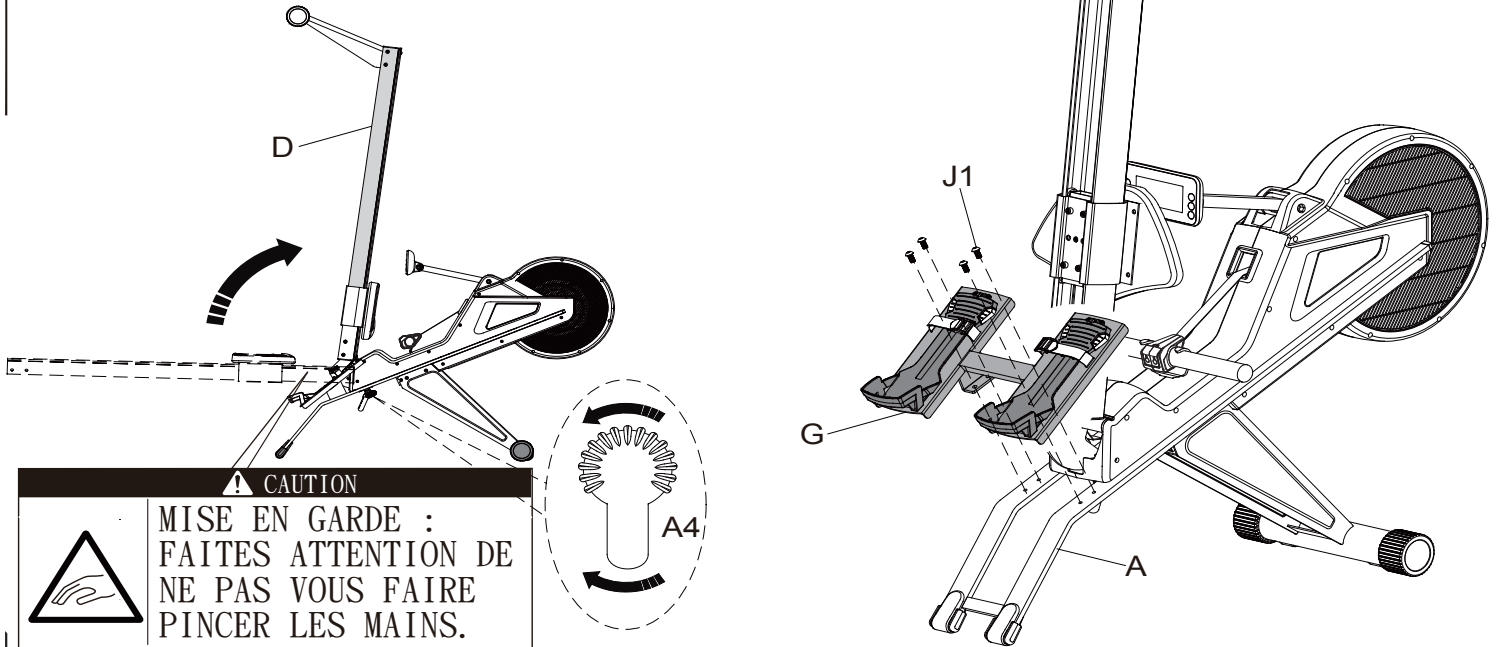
COMMENT ASSEMBLER LE TUBE DE SUPPORT DES PÉDALES
